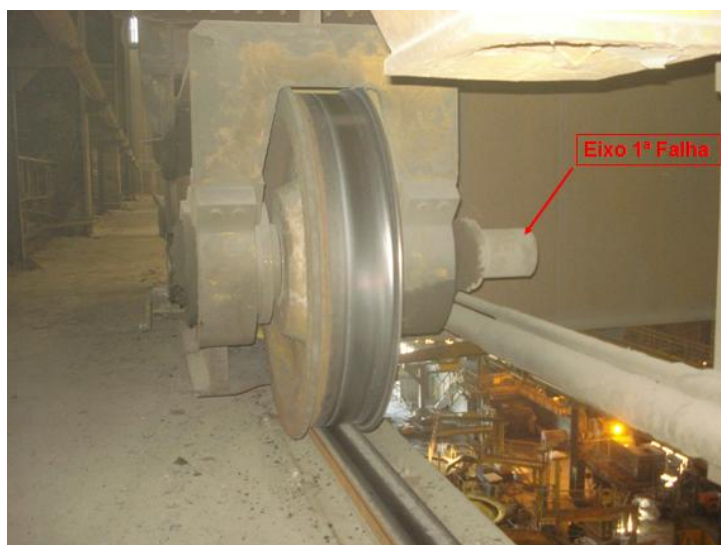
Conjunto Eixo-Roda Livre da 1ª Falha – Translação da Ponte.
